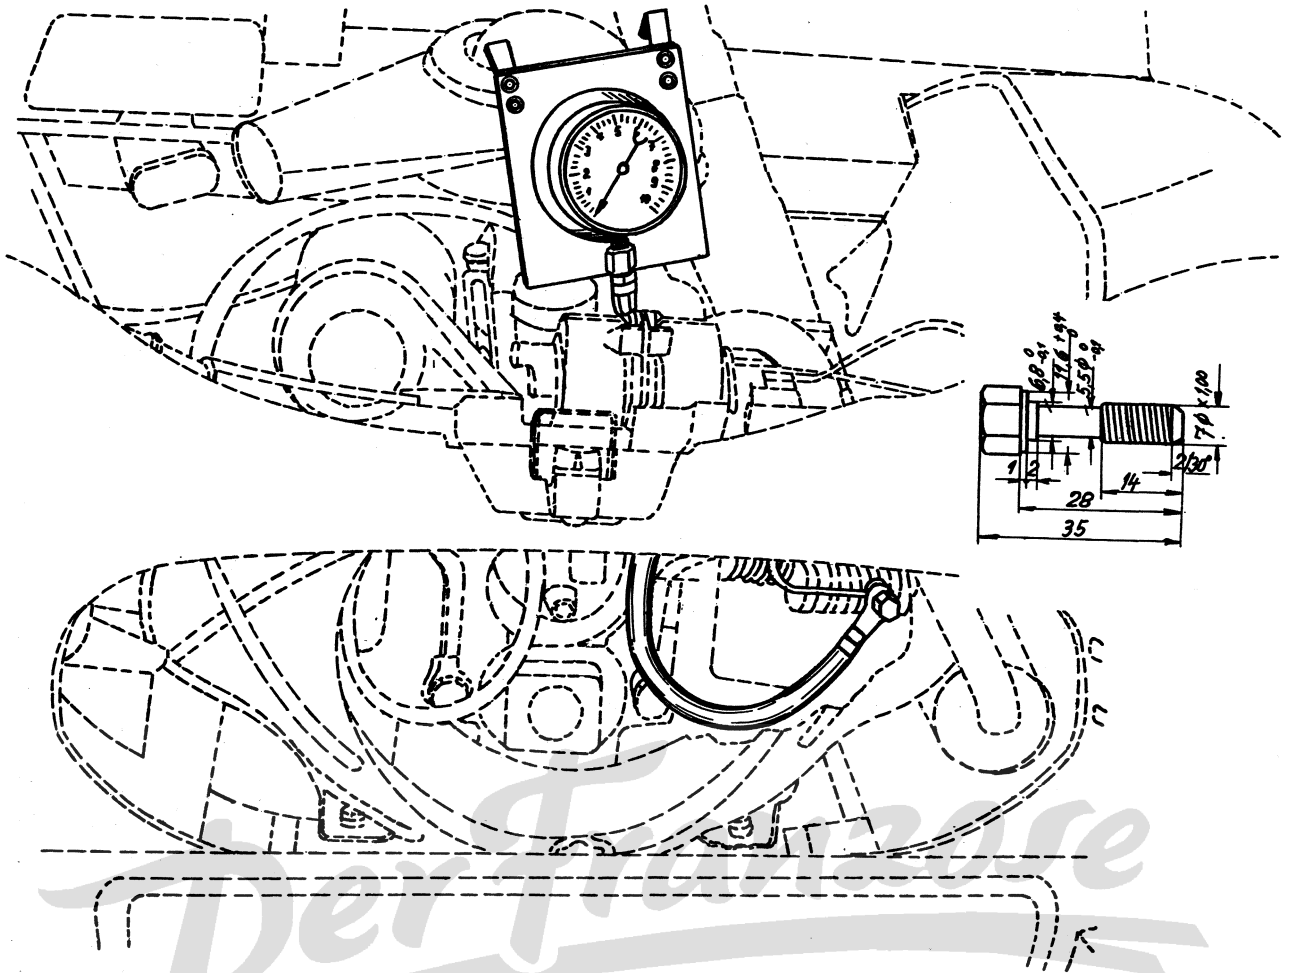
Manometeranschluß für die Kontrolle des Öldruckes
